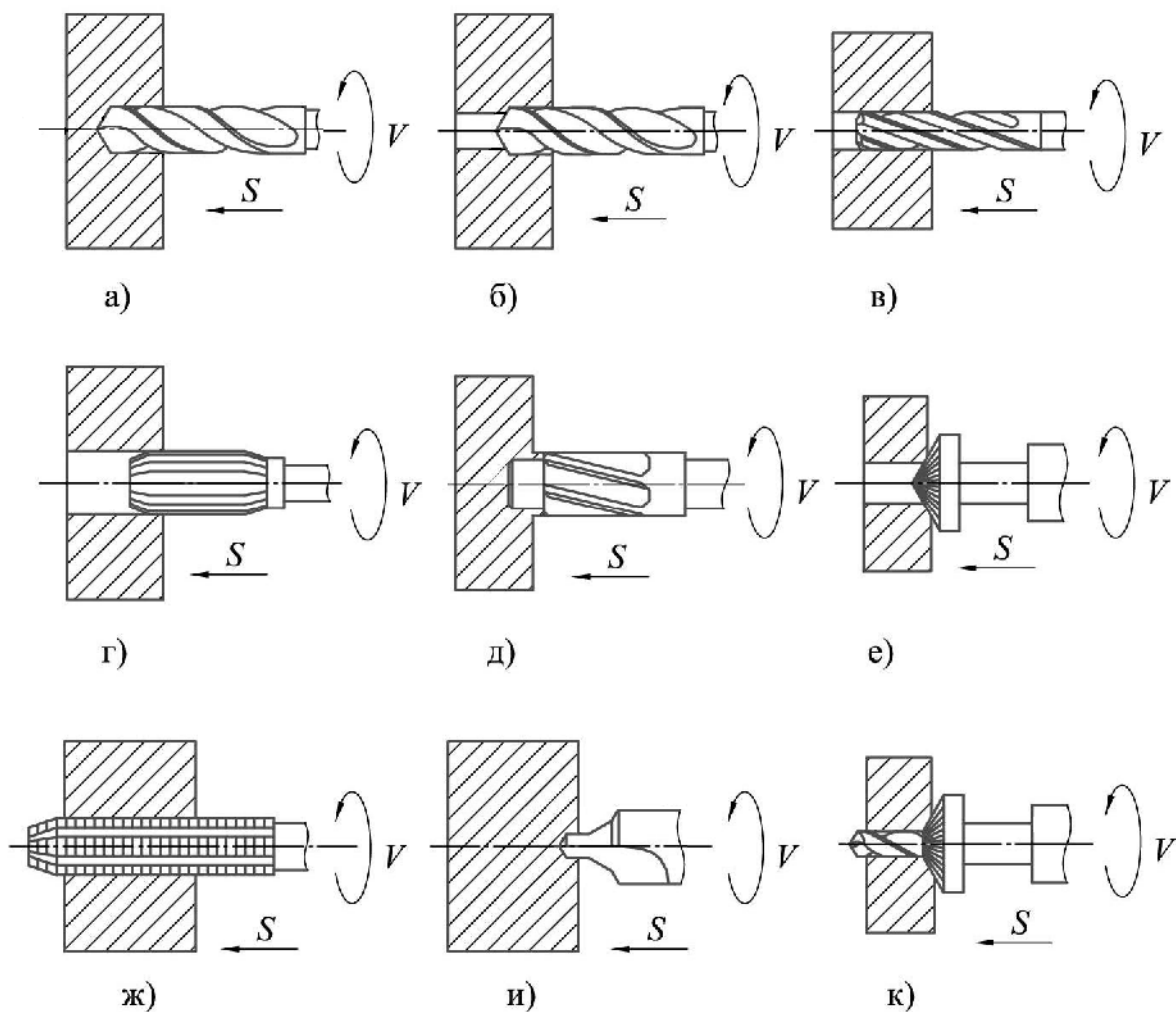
Схеми обробки отворів на свердлильних верстатах
